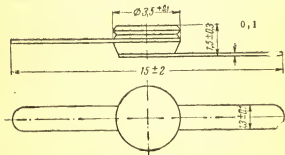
Габаритный чертеж диодов 1И302А — 1И302Г.
